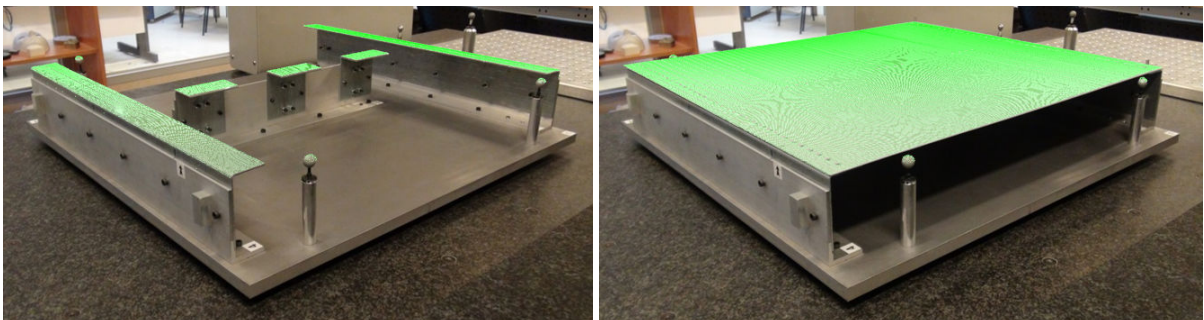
Mesure de l'ensemble support avant l'assemblage et mesure du couvercle assemblé (illustré pour la phase n°1).
